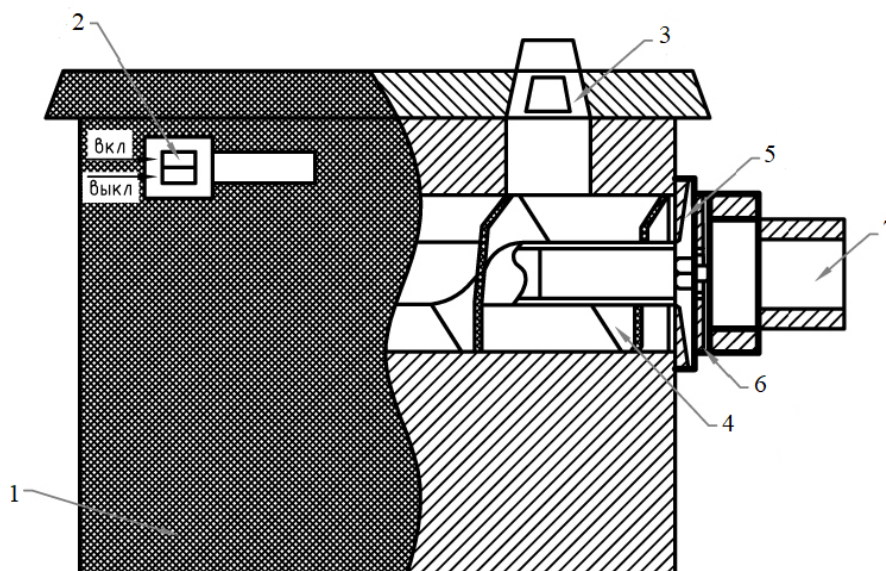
Формующее устройство экструзионного типа: 1 – корпус; 2 – выключатель; 3 – устройство для подачи торфомассы; 4 – диспергирующий и транспортирующий шнек; 5 – четырехлопастной нож; 6 – решетка с фильерами; 7 – формующий мундштук
